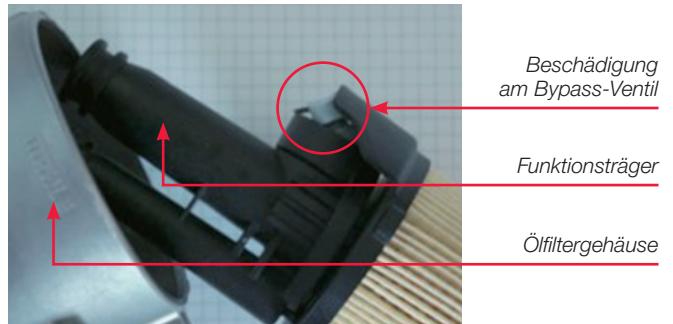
Beschädigung am Bypass-Ventil nach Einbau des Wettbewerber-Nachbaufilters
